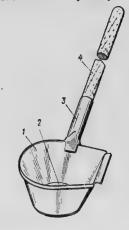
1 — корпус; 2 — дно; 3— тулейка; 4 — ручка
